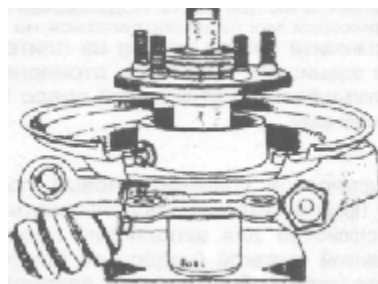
Запрессовка ступицы в корпусе колесного подшипника
